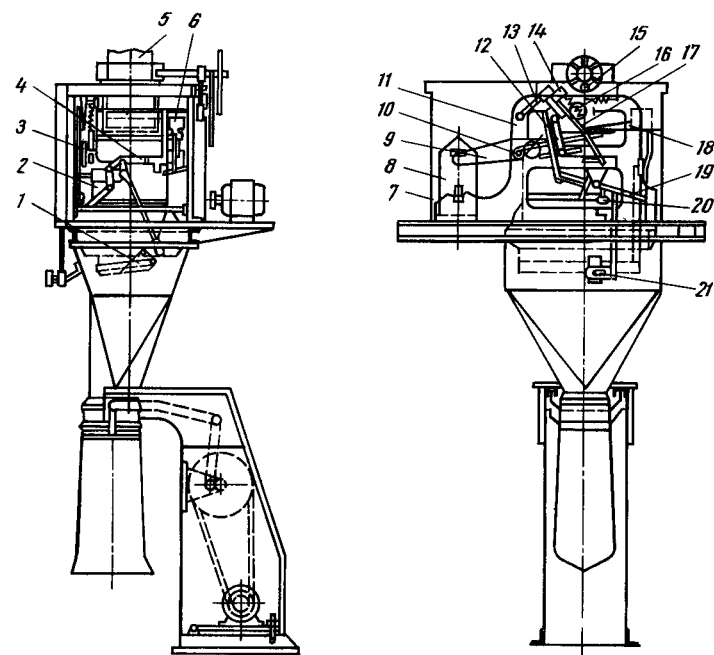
Полуавтоматический весовой дозатор ДВМ-100:
